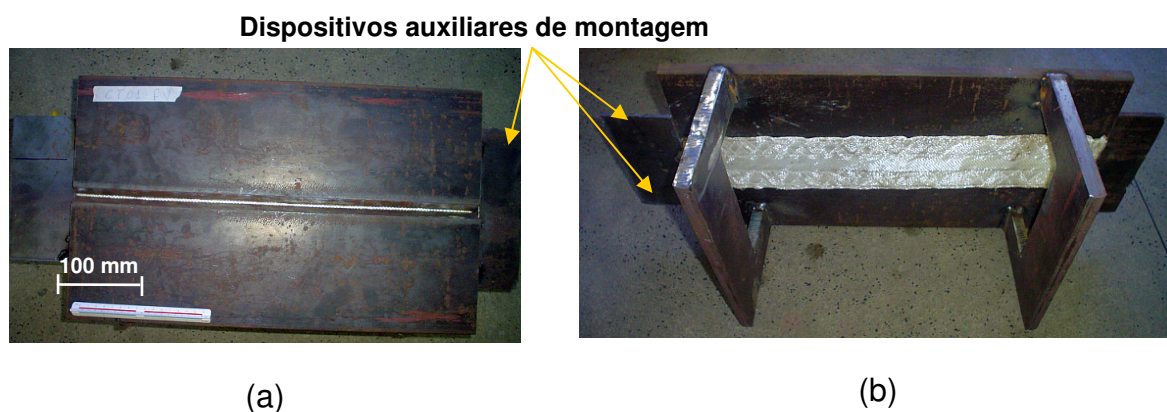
Parte superior (a) e inferior (b) da chapa de teste com suporte de solda fixado
